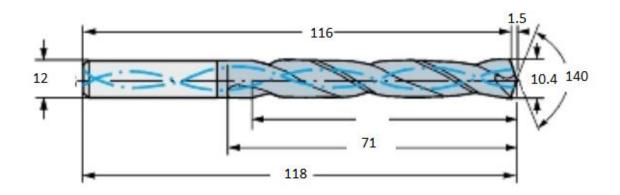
Сверло 460.1-1040-052А1-ХМ GC34
